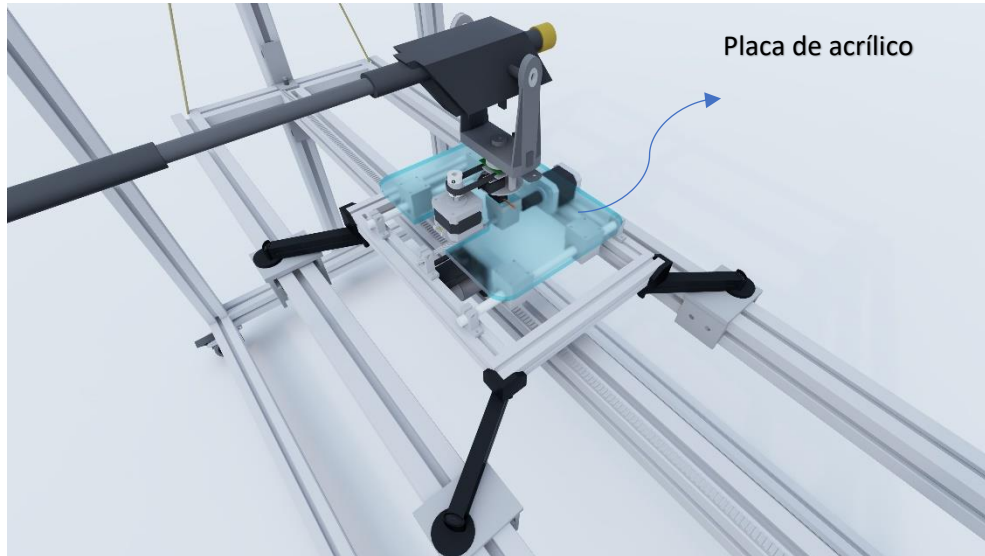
Vista isométrica de la placa de acrílico, el sistema Pan-Tilt y efector final.
